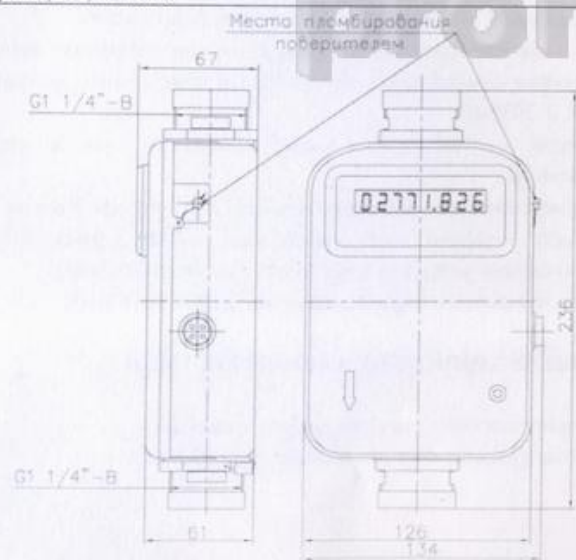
Габаритные, присоединительные размеры счетчика и место пломбирования поверителем
